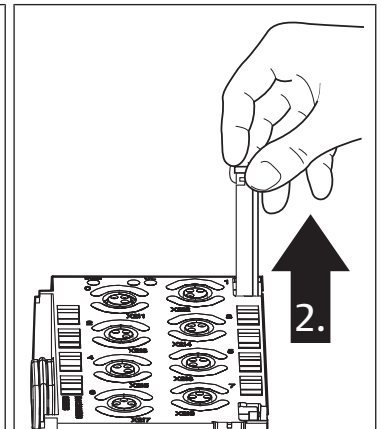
Extracción del elemento de fijación de resorte hacia arriba hasta el tope
